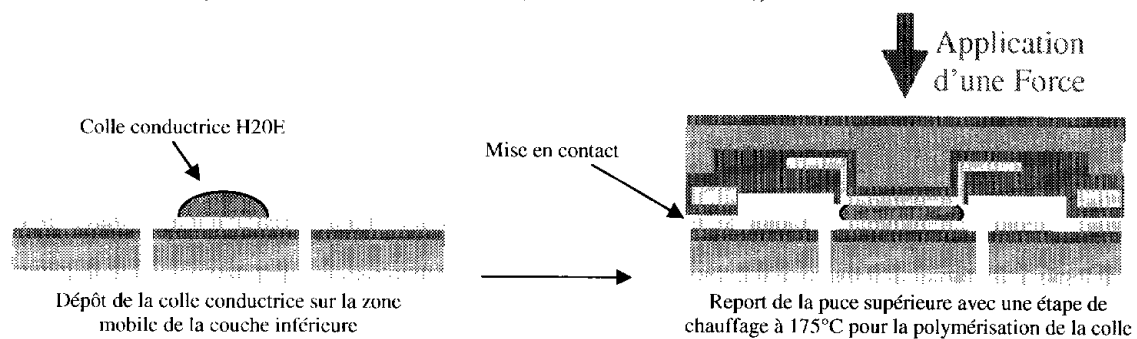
Assemblage des deux couches silicium du capteur par FLIP-CHIP
